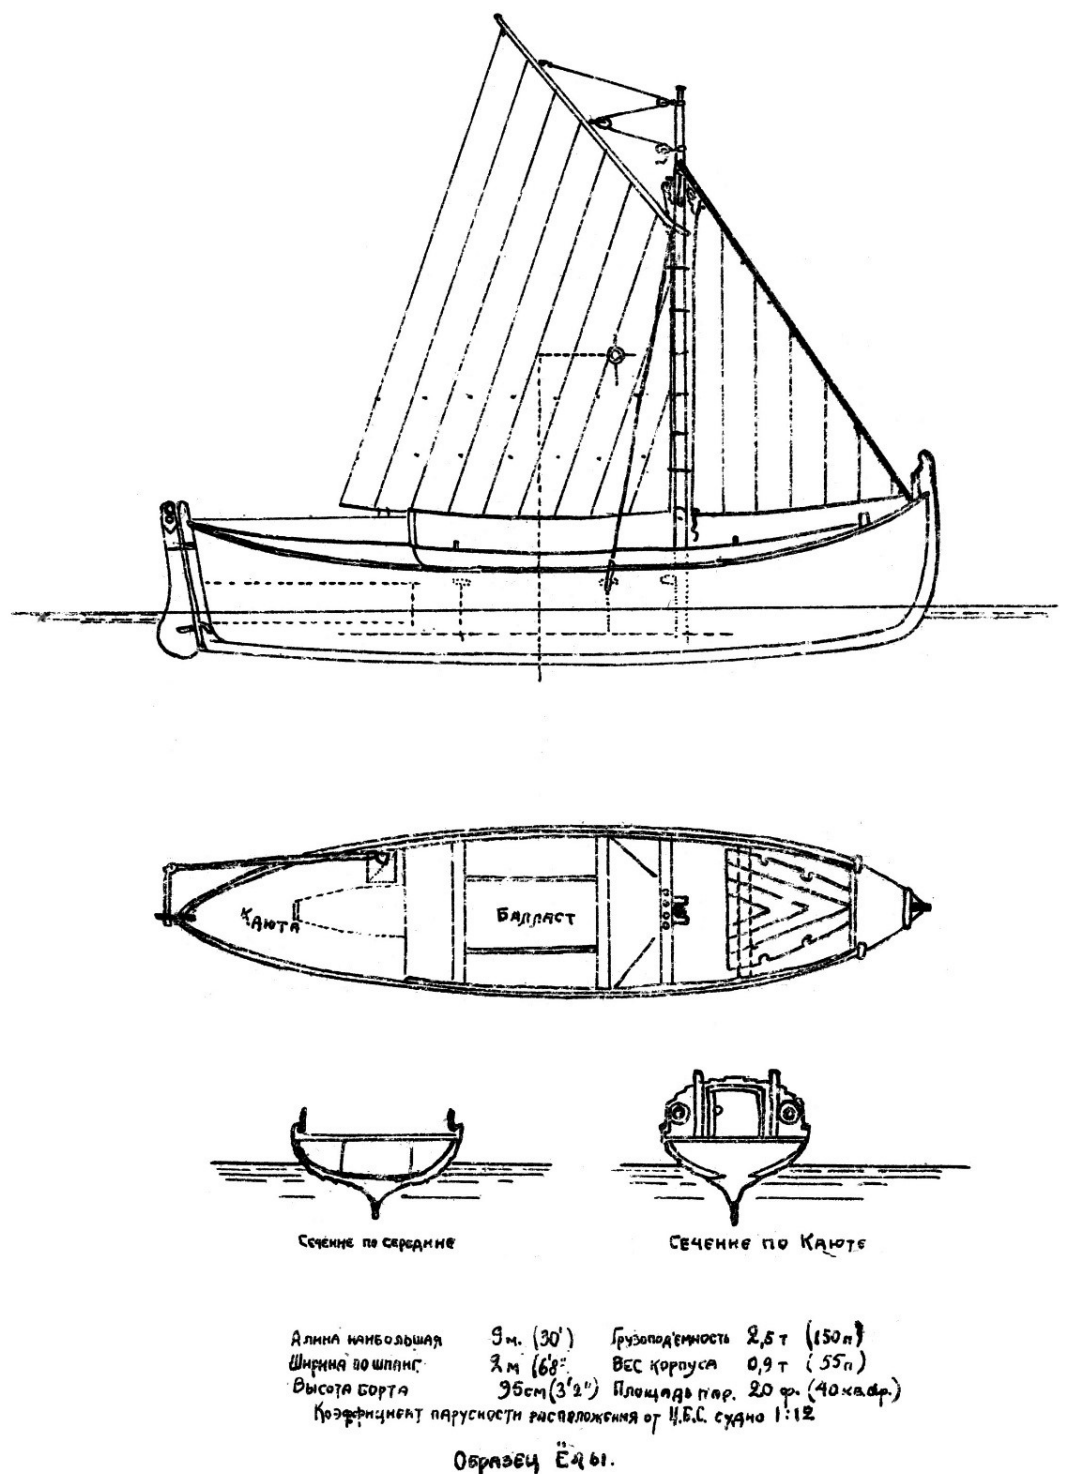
Образец ёлы — эскизный чертеж [Крамаренко, 1925, Прил.]
